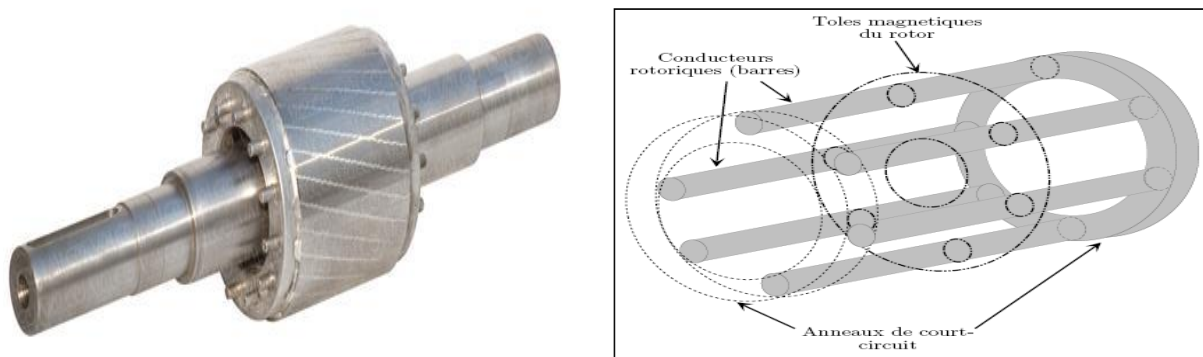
Rotor à cage d'écureuil d'une machine asynchrone.
